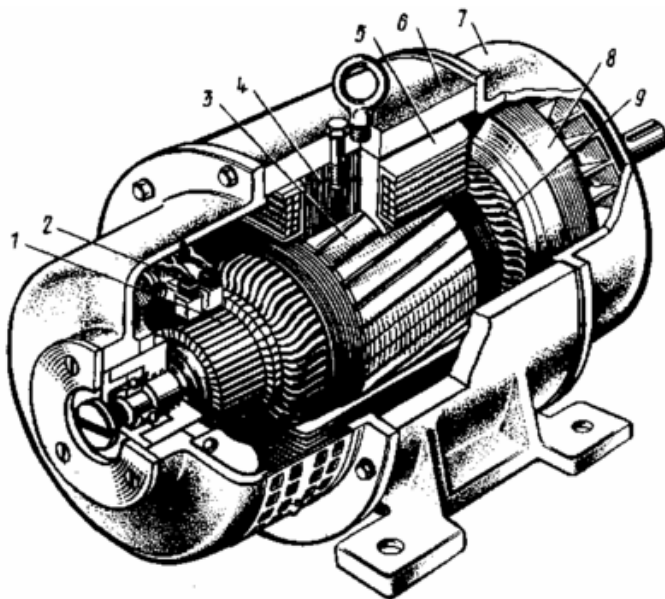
Разрез электрической машины постоянного тока: 1 – коллектор; 2 – щетки; 3 – сердечник якоря; 4 – главный полюс; 5 – катушка обмотки возбуждения; 6 – корпус; 7 – подшипниковый щит; 8 – вентилятор; 9 – обмотка якоря
